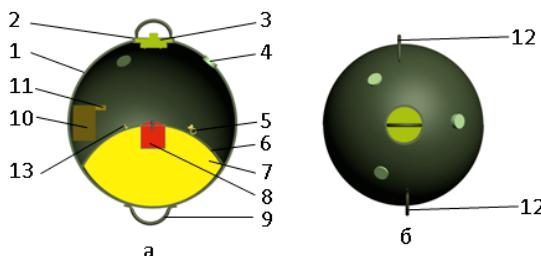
Корпус міни ПДМ-ЗЯ
